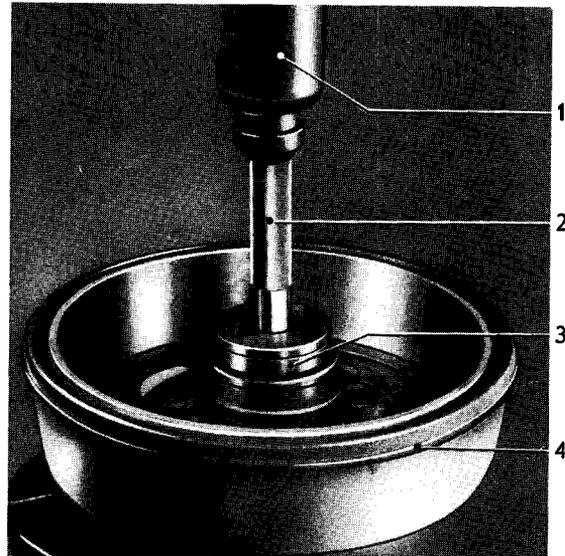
Äußeren Laufring des inneren Radlagers in Radnabe einpressen
